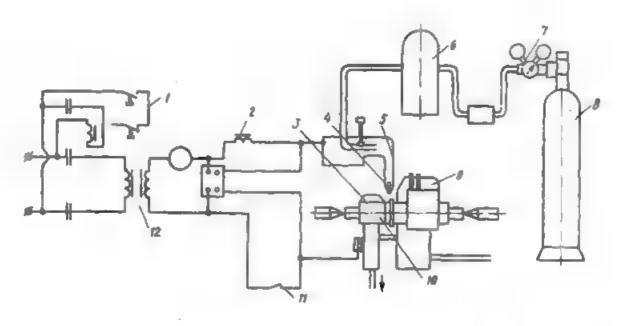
Принциниальная слема установки для аргоно-ауговой сварки концов осиций в петушками коллектора
